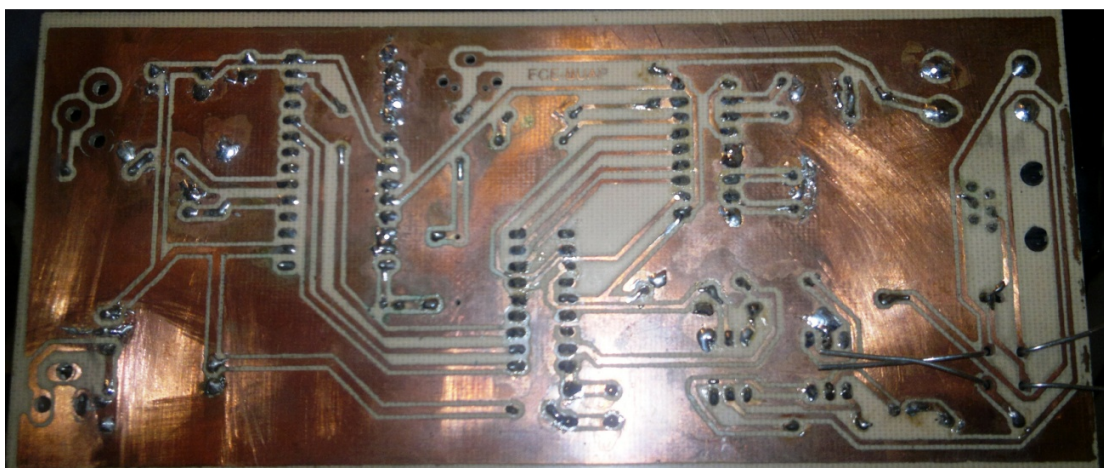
Placa de circuito impreso lado soldaduras.
